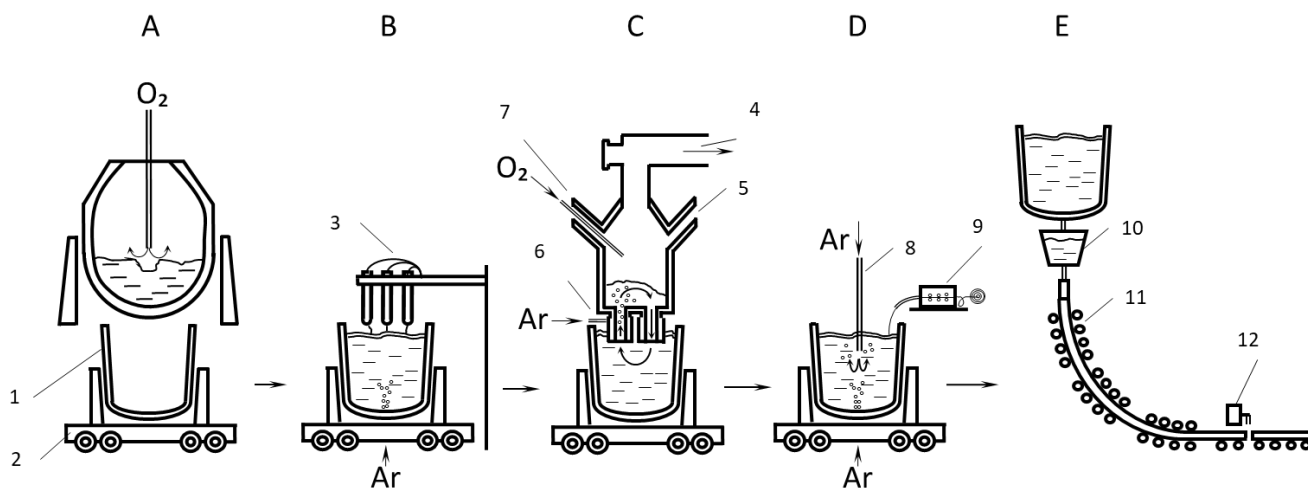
Используемое основное оборудование при выплавке ЭИС в КЦ-1 ПАО «НЛМК»: А – Конвертер; В – УПК (установка печь-ковш); С – АЦВ (агрегат циркуляционного вакуумирования); D – УДМ (установка доводки металла); Е – УНРС (установка непрерывной разливки стали);
